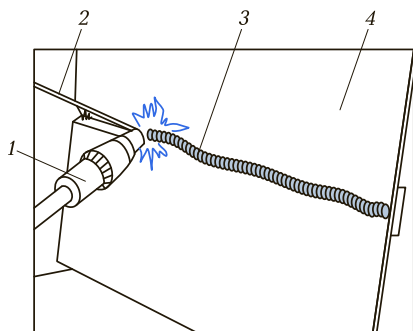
Сварка в горизонтальном положении:
